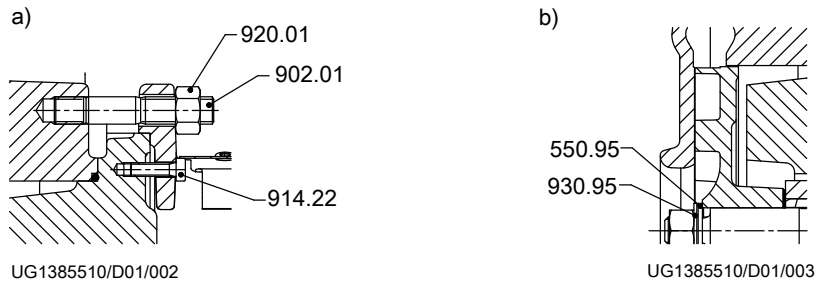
a) Gehäusedeckel geklemmt, b) Laufradbefestigung bei Welleneinheit 25
